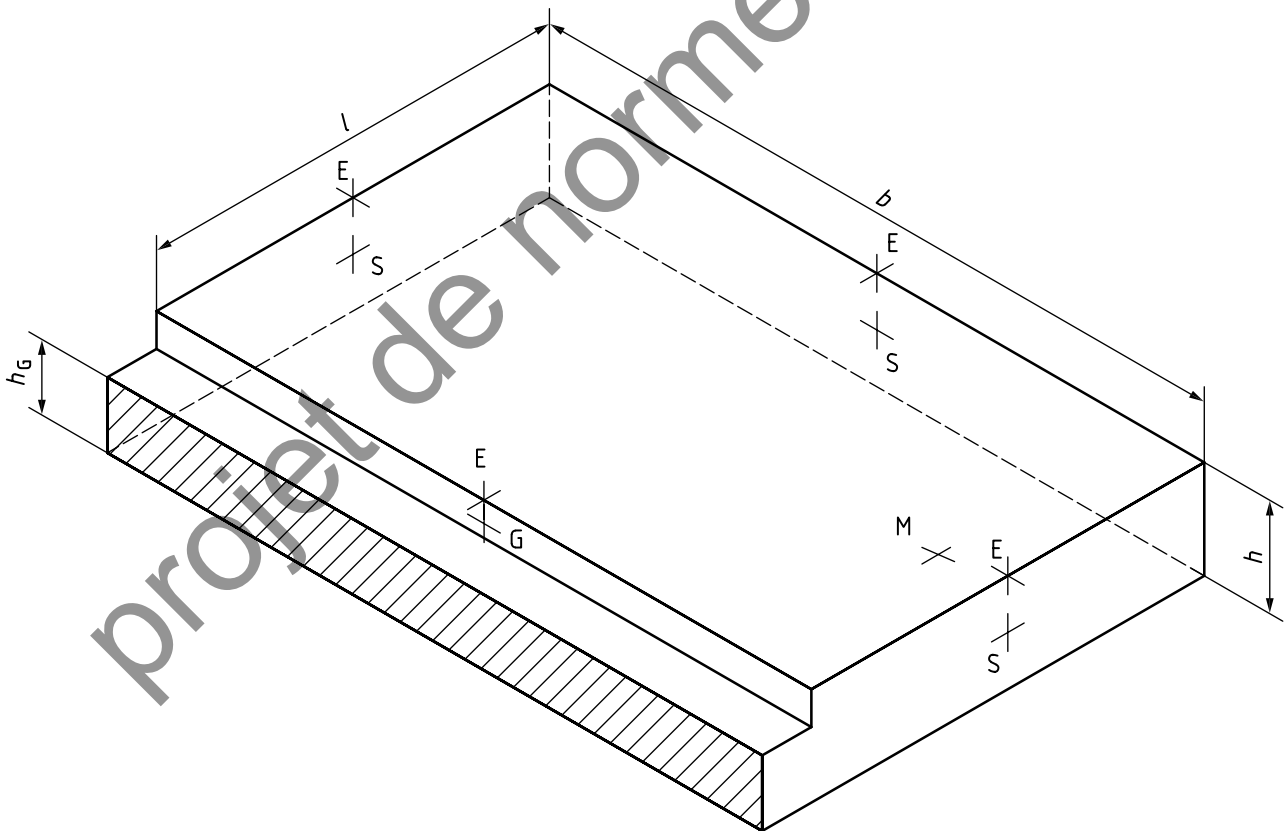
Vue en perspective d'une plaque moulée par injection
